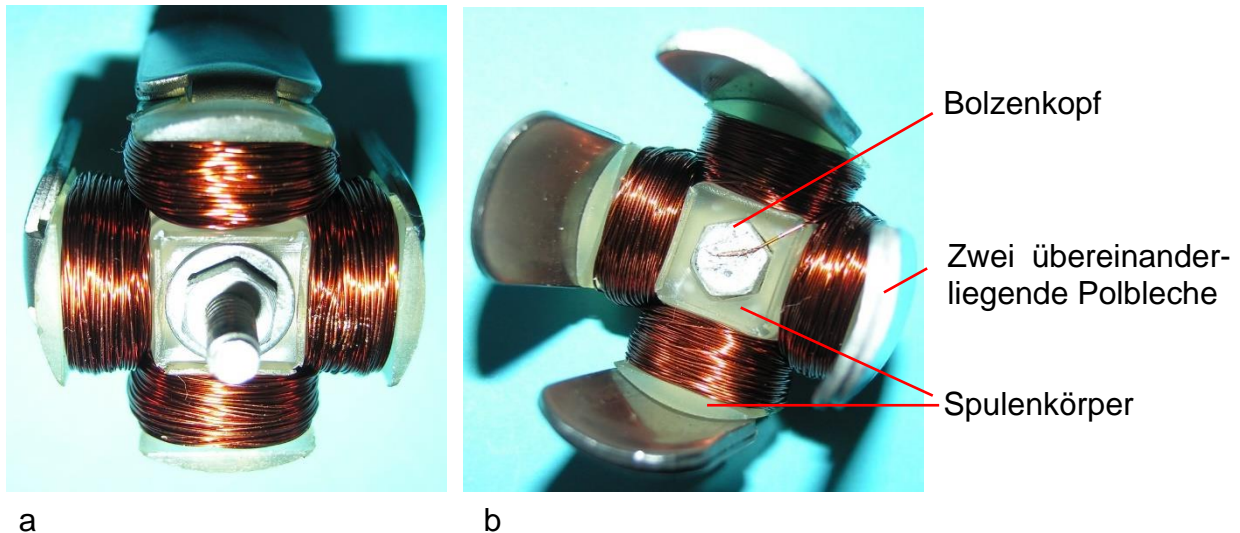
Anker mit Kabelanschlussbolzen: a) Bolzenende zur Aufnahme der Klemmelemente, b) Bolzenkopf mit dem spannungführenden Spulenkörper
